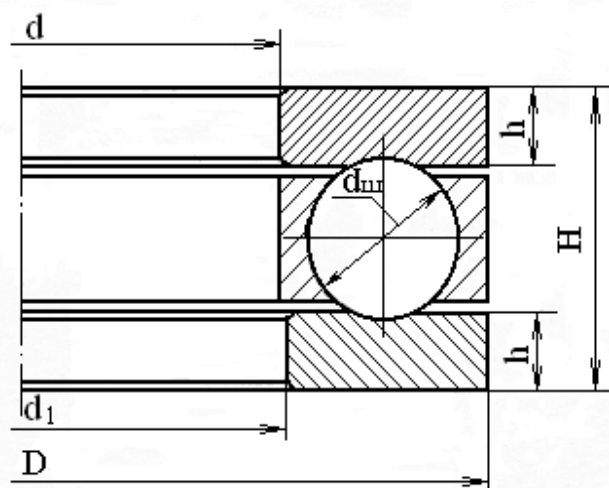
Подшипник шариковый упорный, однорядный
